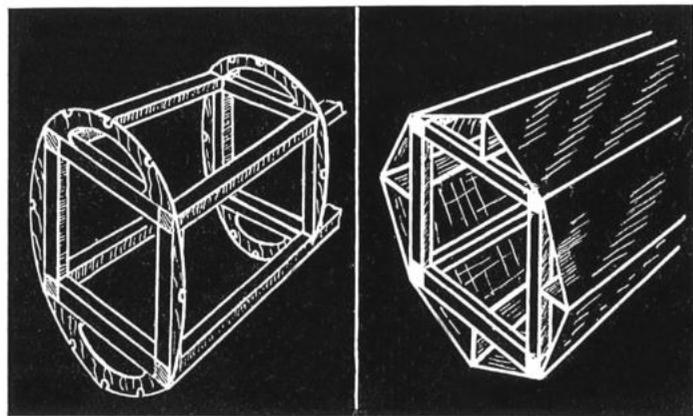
Da un traliccio base a sezione quadra si possono ottenere fusoliere di sezione differente.
